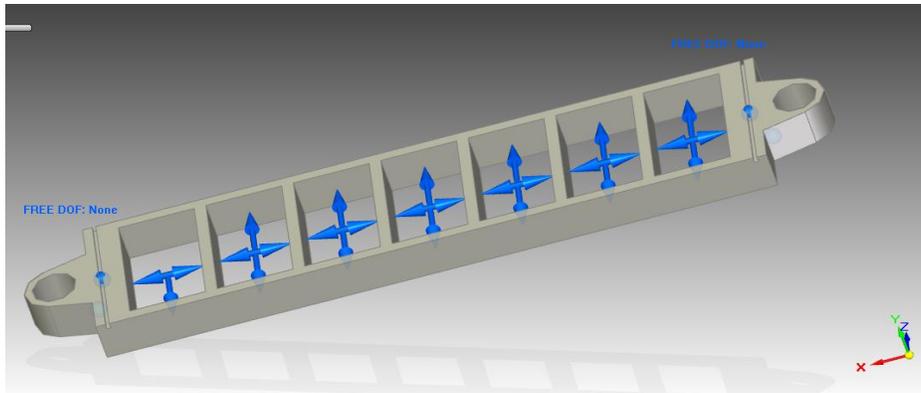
vista de la rejilla de moldeo, se ilustra cómo actúan las fuerzas de compresión sobre las caras internas
